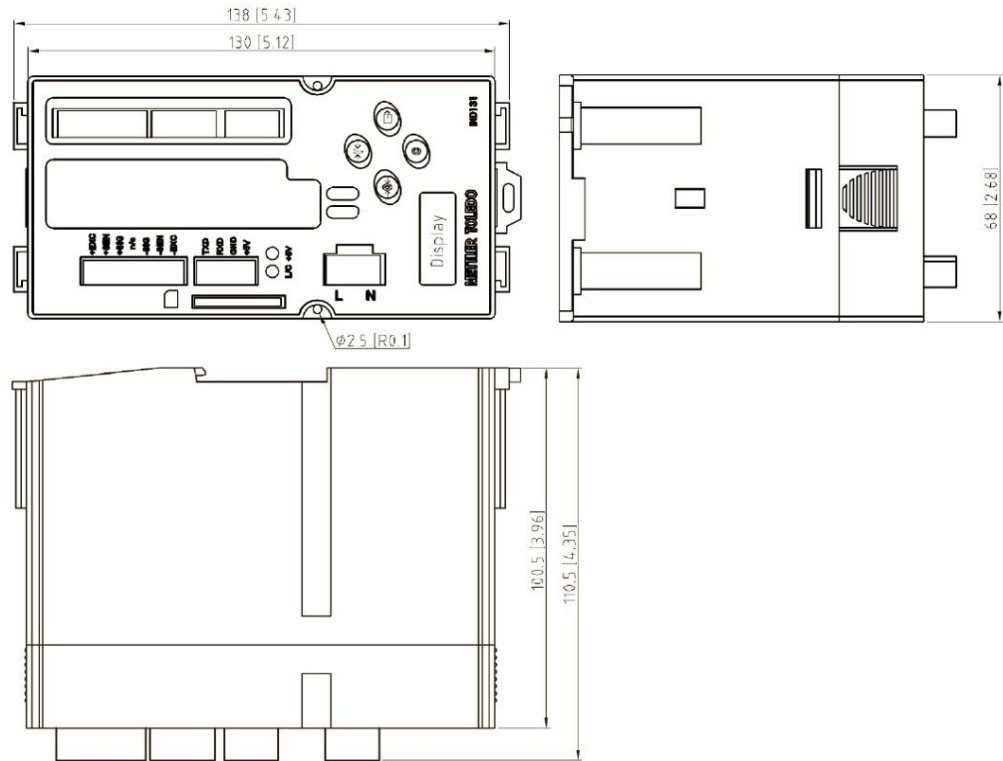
Dimensões de gabinete de montagem em trilho IND131 DIN
